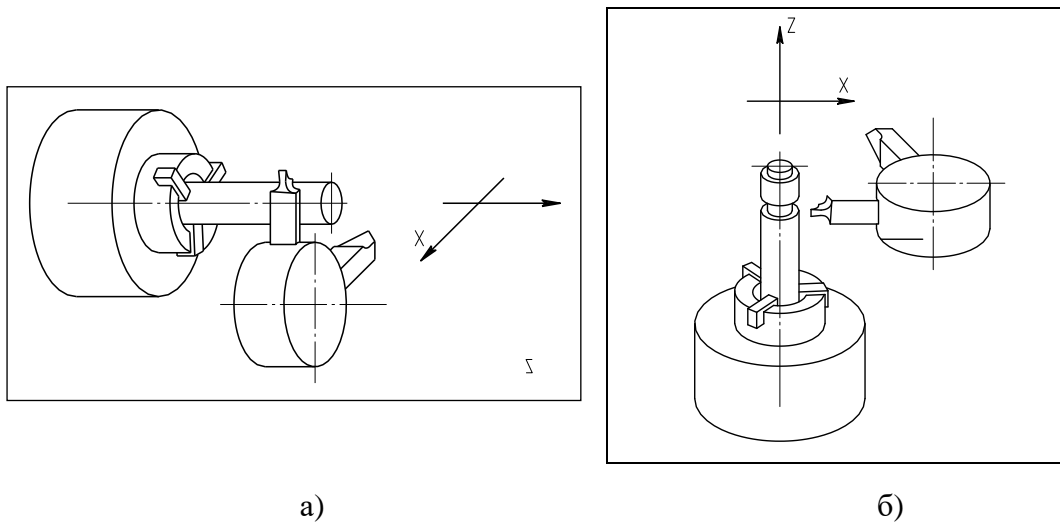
Система координат токарного верстата з горизонтальним (а) і вертикальним (б) розташуванням шпинделя
